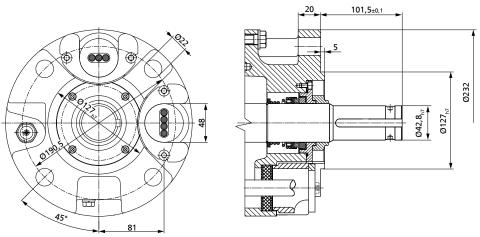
Dimensiones de conexión de UMA 250, UMA-S 250, dimensiones indicadas en [mm]
